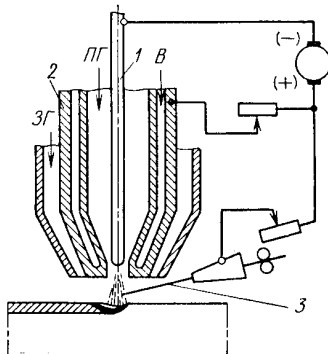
Плазменно-порошковая наплавка с токоведущей присадочной проволокой:
